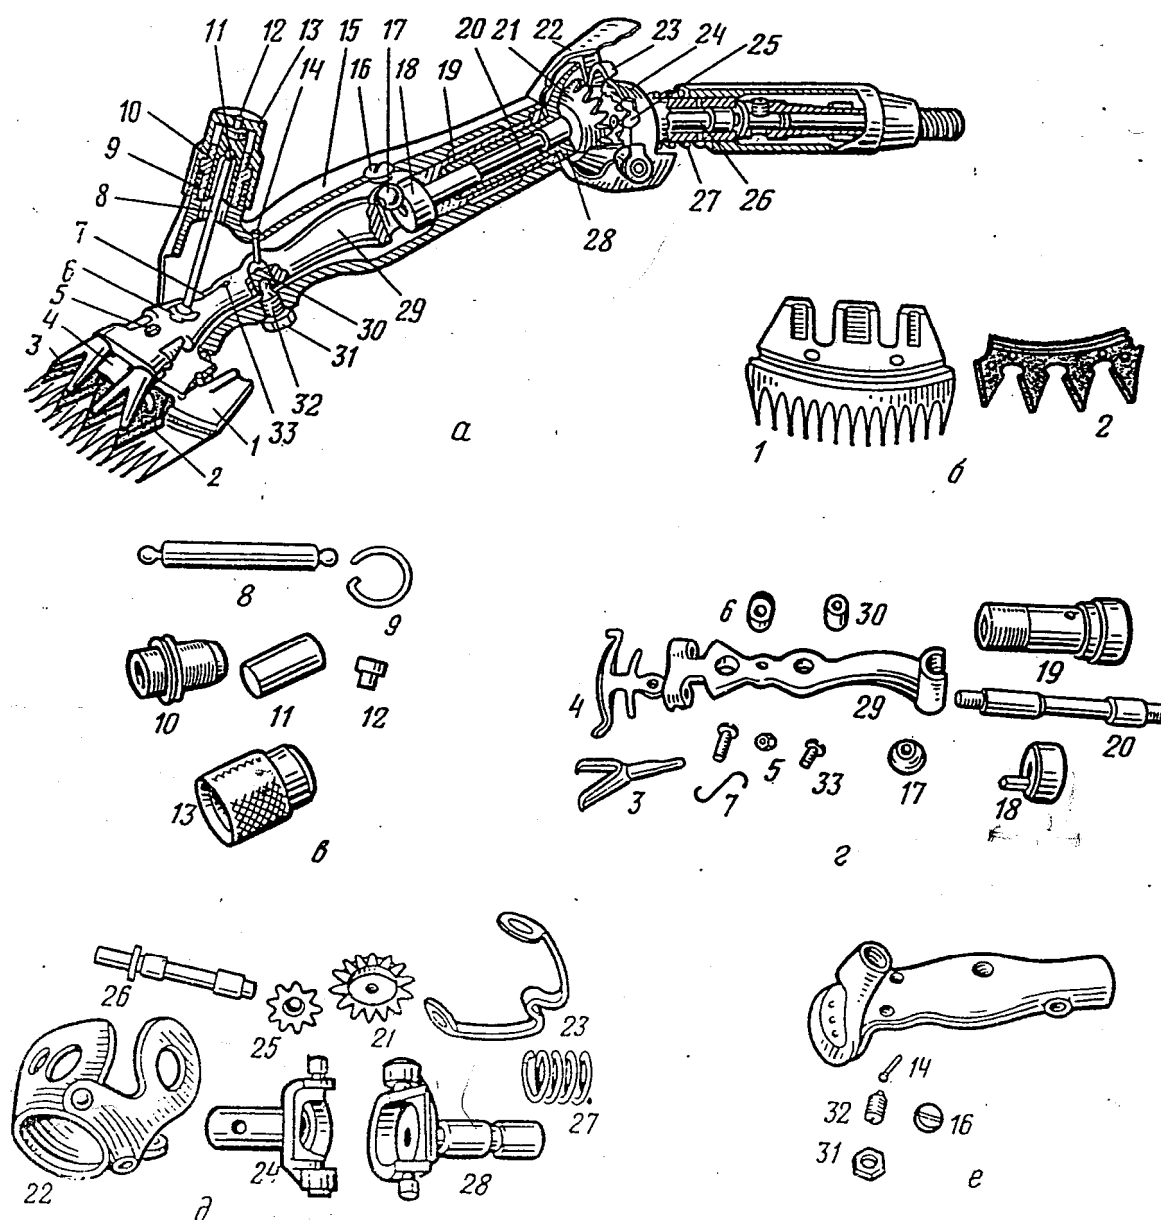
Общий вид (а) машинки МСО-77Б для стрижки овец и детали режущего аппарата (б), нажимного (в), эксцентрикового (г), шарнирного (д) механизмов и корпуса (е): 1 - гребенка; 2 - нож; 3 - нажимная лапка; 4 - пружина нажимных лапок; 5 - гайка; 6 - подпятник стержня; 7, 27 - пружины; 8 - упорный стержень; 9 - стопорная пружина; 10 - штуцер; 11 - нажимной патрон; 12 - упор патрона; 13 - нажимная гайка; 14 - предохранительный винт; 15 - корпус; 16 - заглушка; 17 - ролик; 18 - эксцентрик; 19 - втулка; 20 - валик; 21 - большая шестерня; 22 - наружный кожух; 23 - замок шарнира; 24 - наружный кожух шарнира; 25 - малая шестерня; 26 - передаточный валик; 28 -
